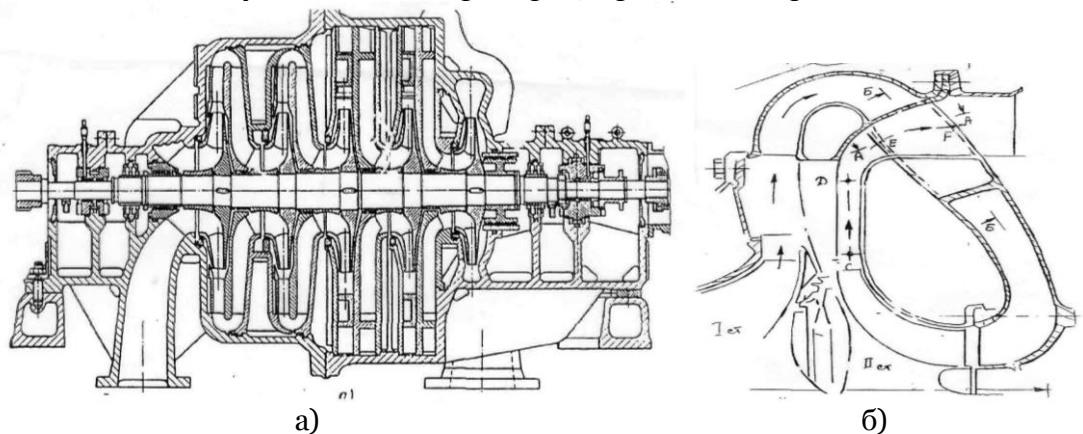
а), Цилиндр низкого давления компрессора НЗЛ [6],
